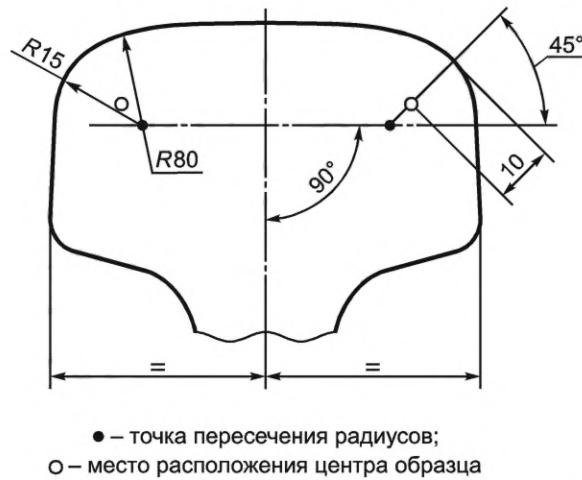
Схема расположения центра образца для испытания на растяжение
